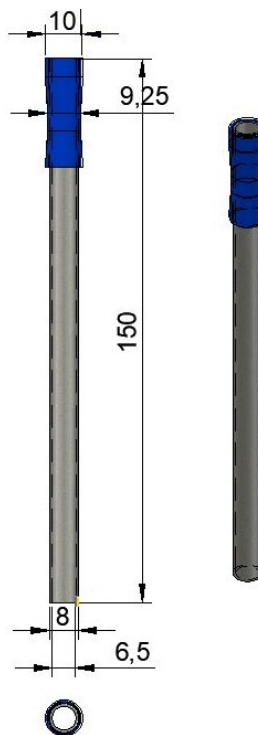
Ukázka chapadla transferu před seřizováním (Vlastní zpracování)
